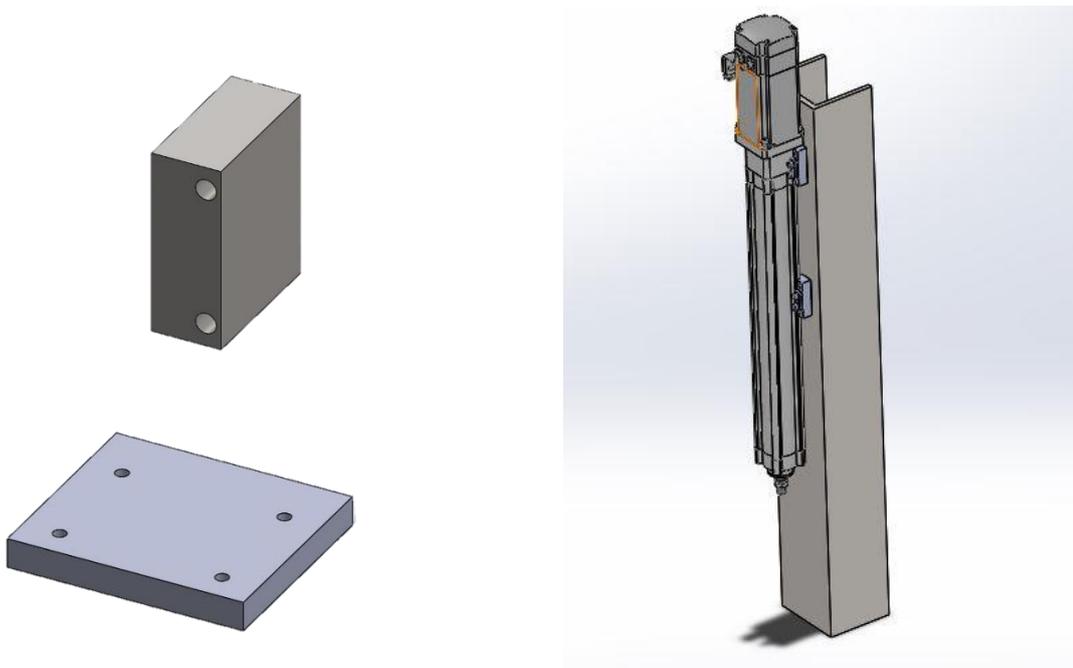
Arriba a la izquierda, el diseño 3D del espaciador. Abajo a la izquierda, el diseño 3D de la placa base. A la derecha, diseño 3D del ensamblaje del electrocilindro con la pieza de sujeción.
